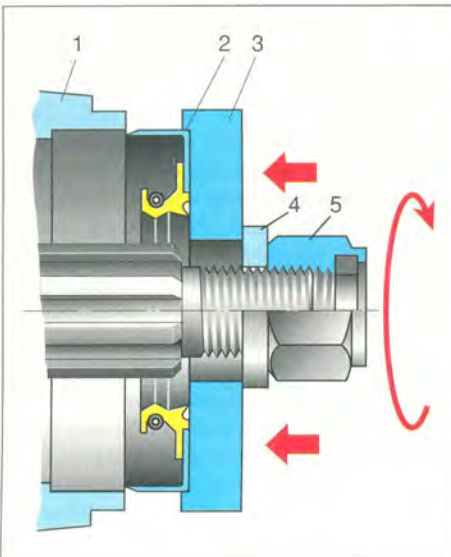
Запрессовка нового сальника: 1 – корпус; 2 – сальник; 3 – оправка; 4 – шайба; 5 – гайка.
